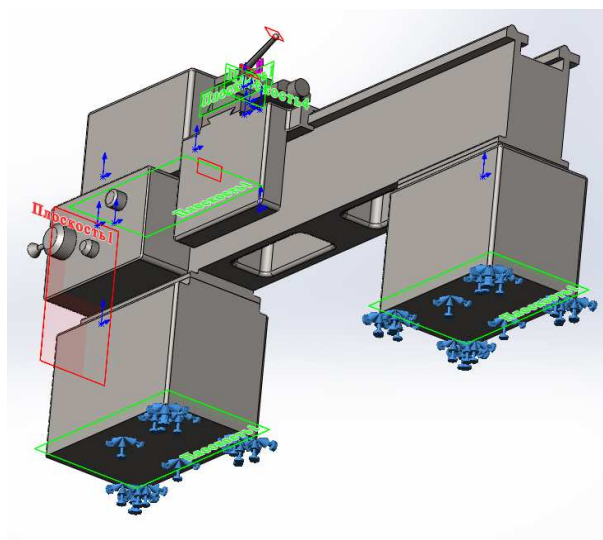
Схема жорсткого монтажу верстата на фундаменті
